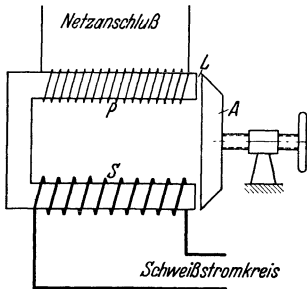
Schweißumspanner mit Luftspaltregelung.
